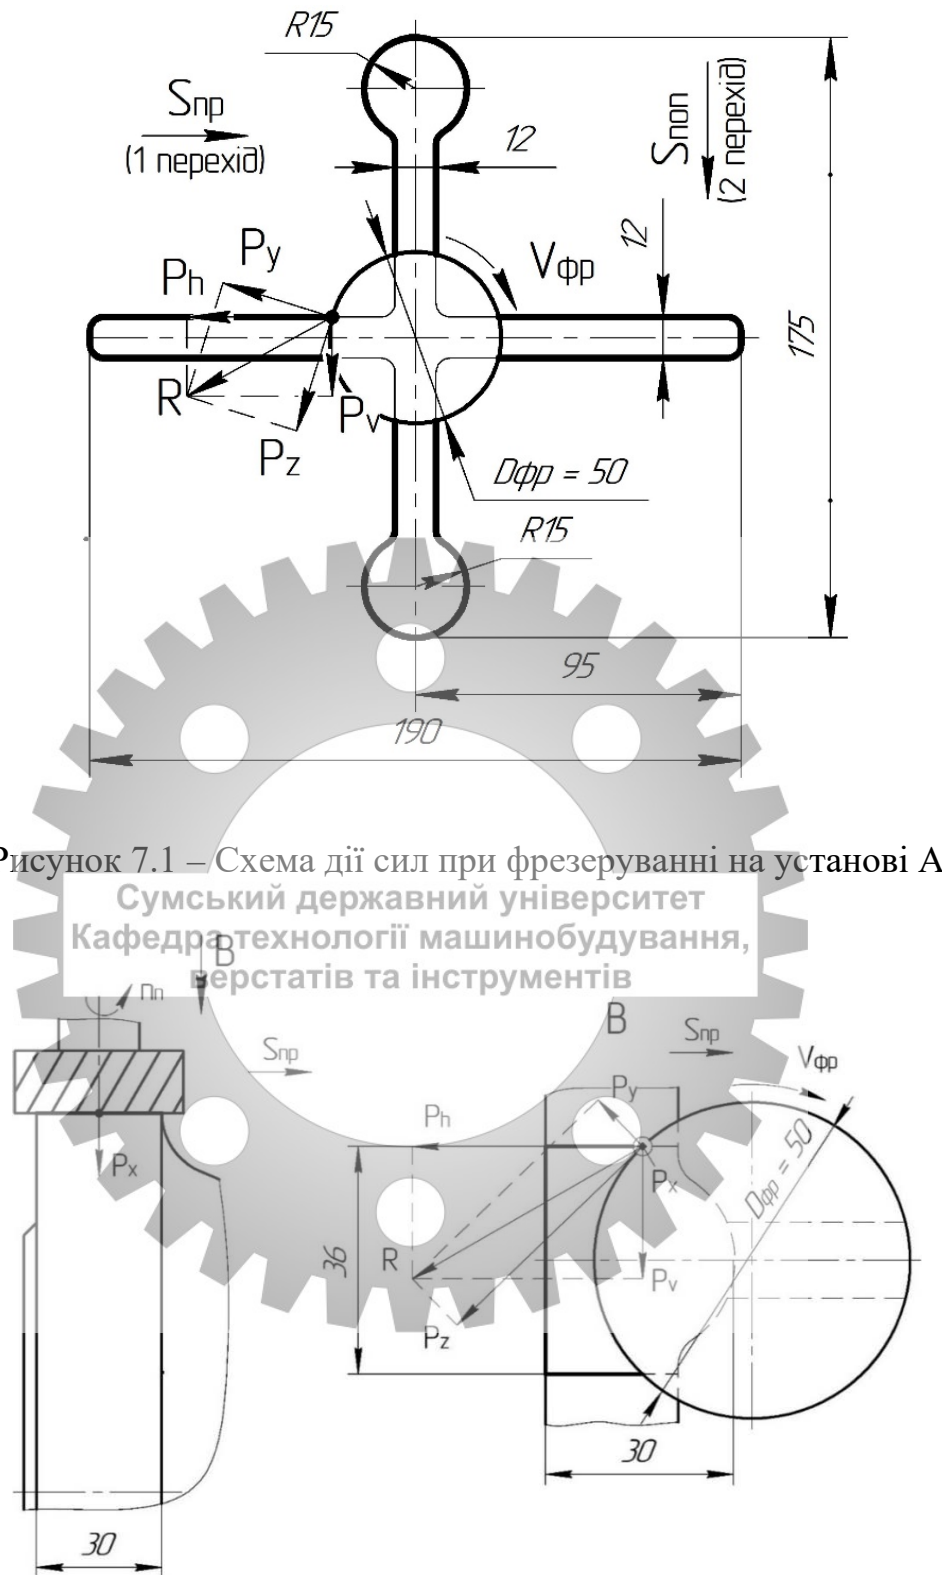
Схема дії сил при фрезеруванні на установі А
